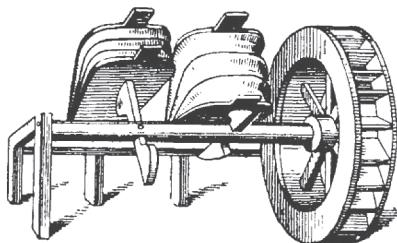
Кулачковый привод от водяного колеса к двум воздуходувным мехам для получения непрерывного дутья.
